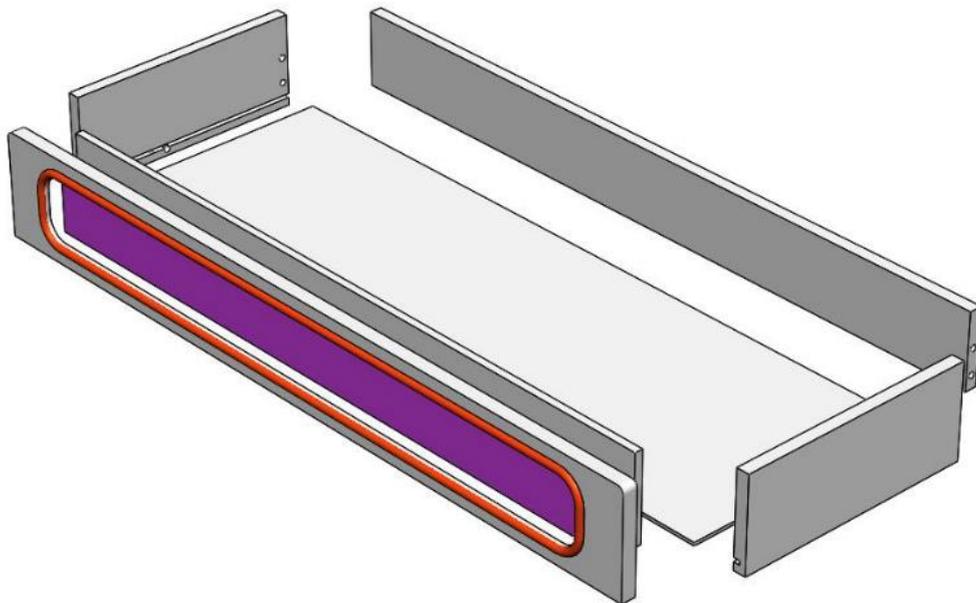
Gaveta superior em vista isométrica com vista explodida.
